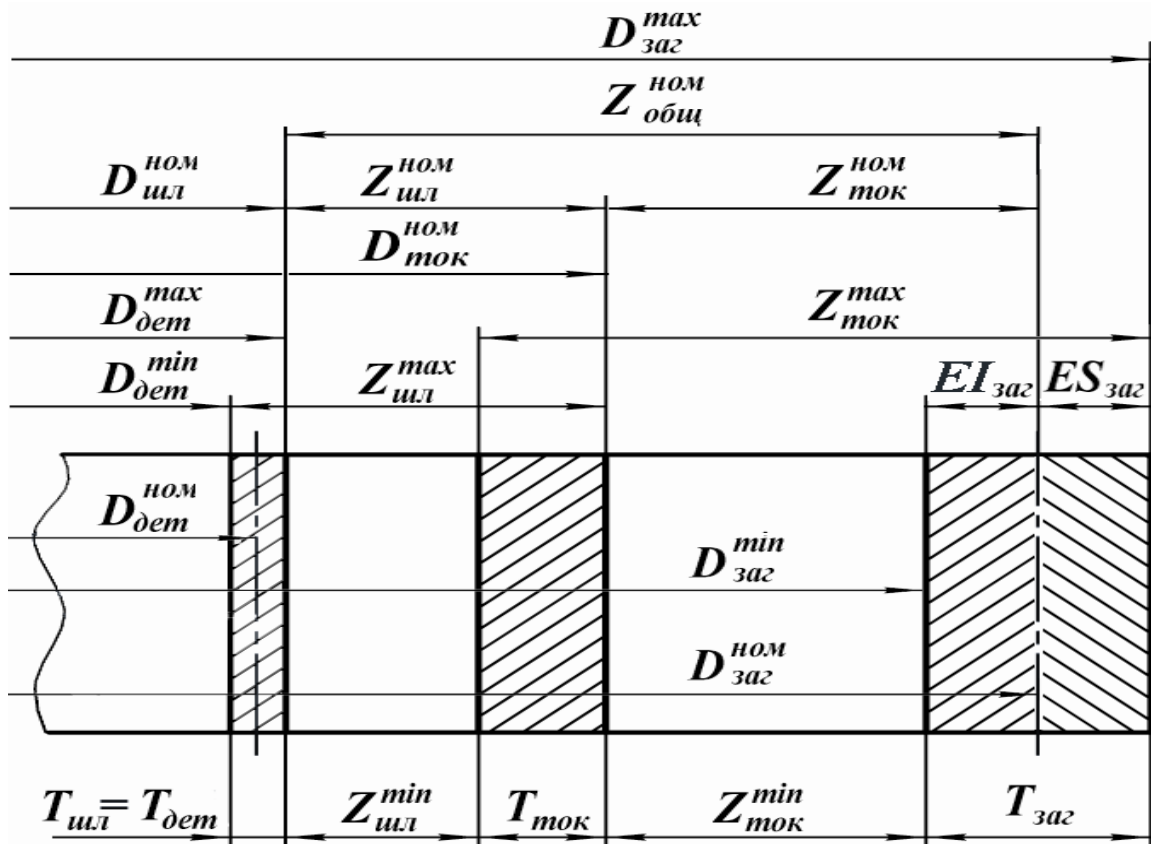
Схема расположения припусков и допусков на операции точения и шлифования вала
